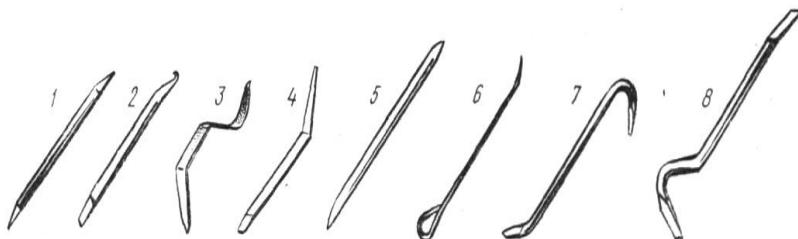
Рычаги и прижимы для исправления вмятин: 1-рычаг для исправления дефектов штамповки; 2-рычаг для рихтовки крыльев после окраски; 3-рычаг-прижим; 4-рычаг для исправления вмятин; 5-рычаг пластинчатый для исправления вмятин в труднодоступных местах; 6-рычаг для исправления разных дефектов; 7-рычаг для предварительной правки; 8-рычаг для устранения больших деформаций
